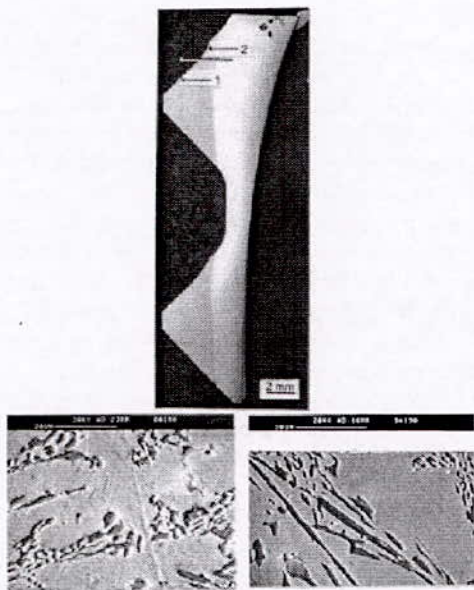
Coupe macroscopique, vue de la surface et coupe microscopique d'un cliquet usé
